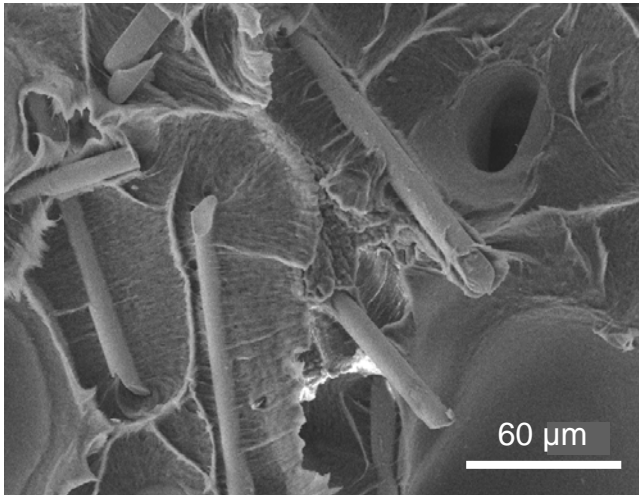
REM-Bruchflächenaufnahme der Schweißnaht von 10/20.
